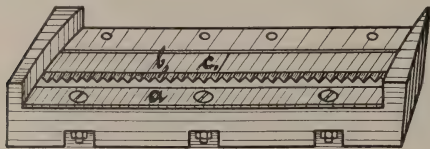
Messerkasten einer Rübenschnitzelmaschine.
